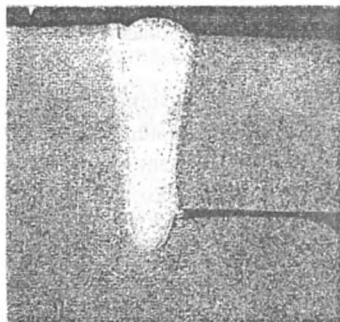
Микрошлиф сварного соединения, полученного на оптимальных режимах сварки
